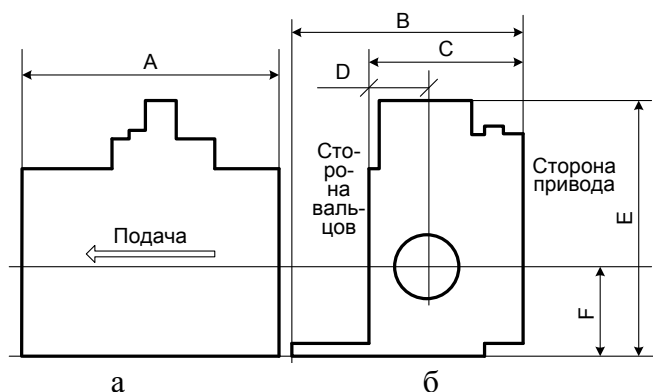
Габаритные размеры станков Nicholson A5B:
